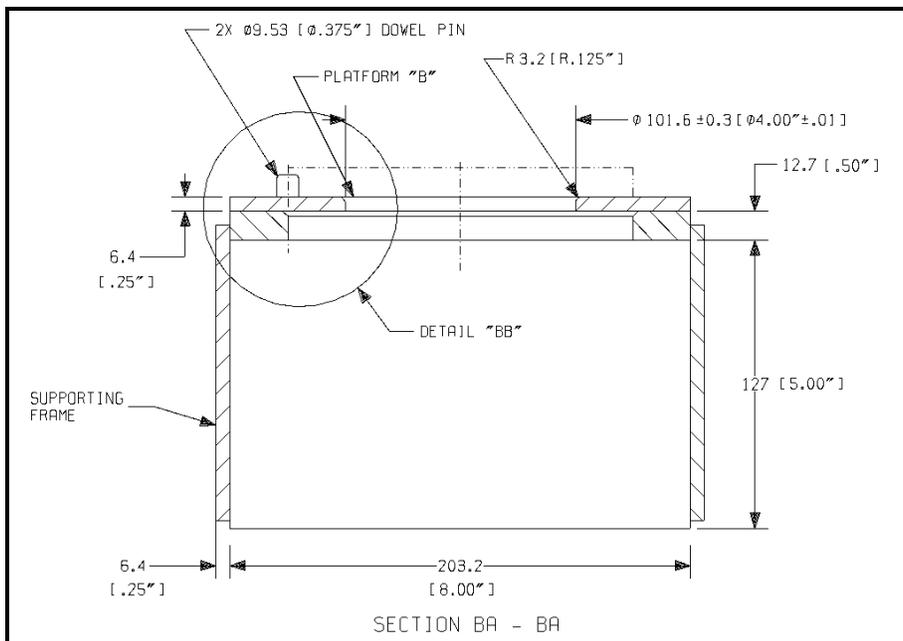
Montage d'essai : Bâti-support et plateforme : Section BA-BA de la section BB de la figure 16
